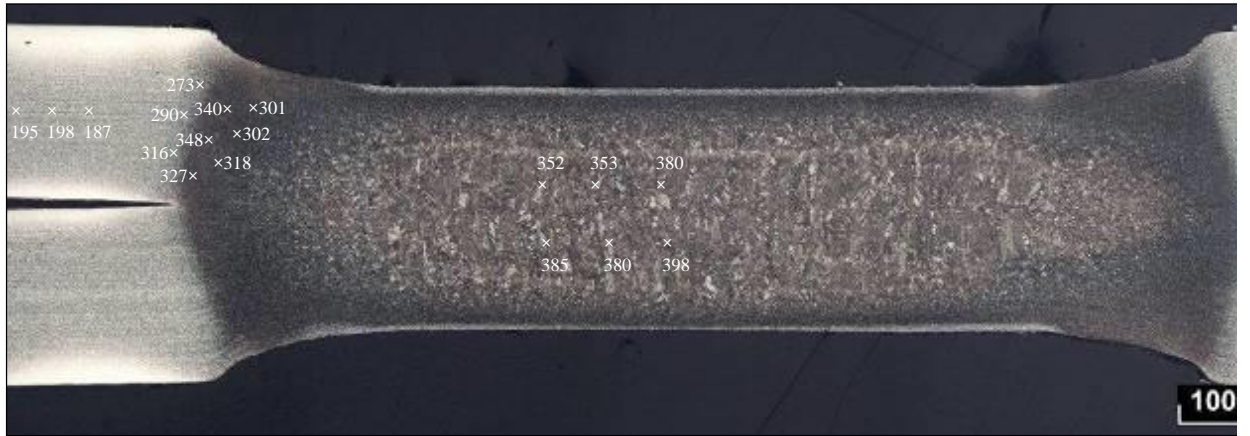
Схема замеров твердости HV1 сварной точки 5.1.1
